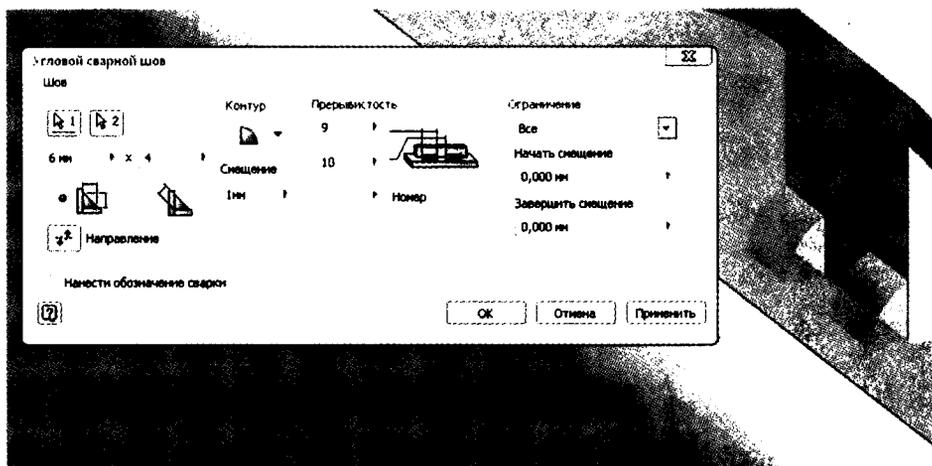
Предпросмотр прерывистого сварного шва
